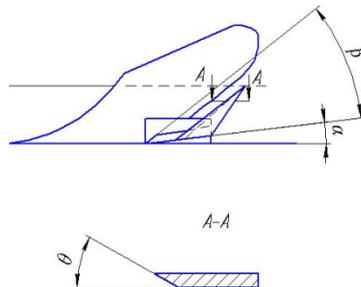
Корпус плуга с горизонтальным и вертикальным ножами
